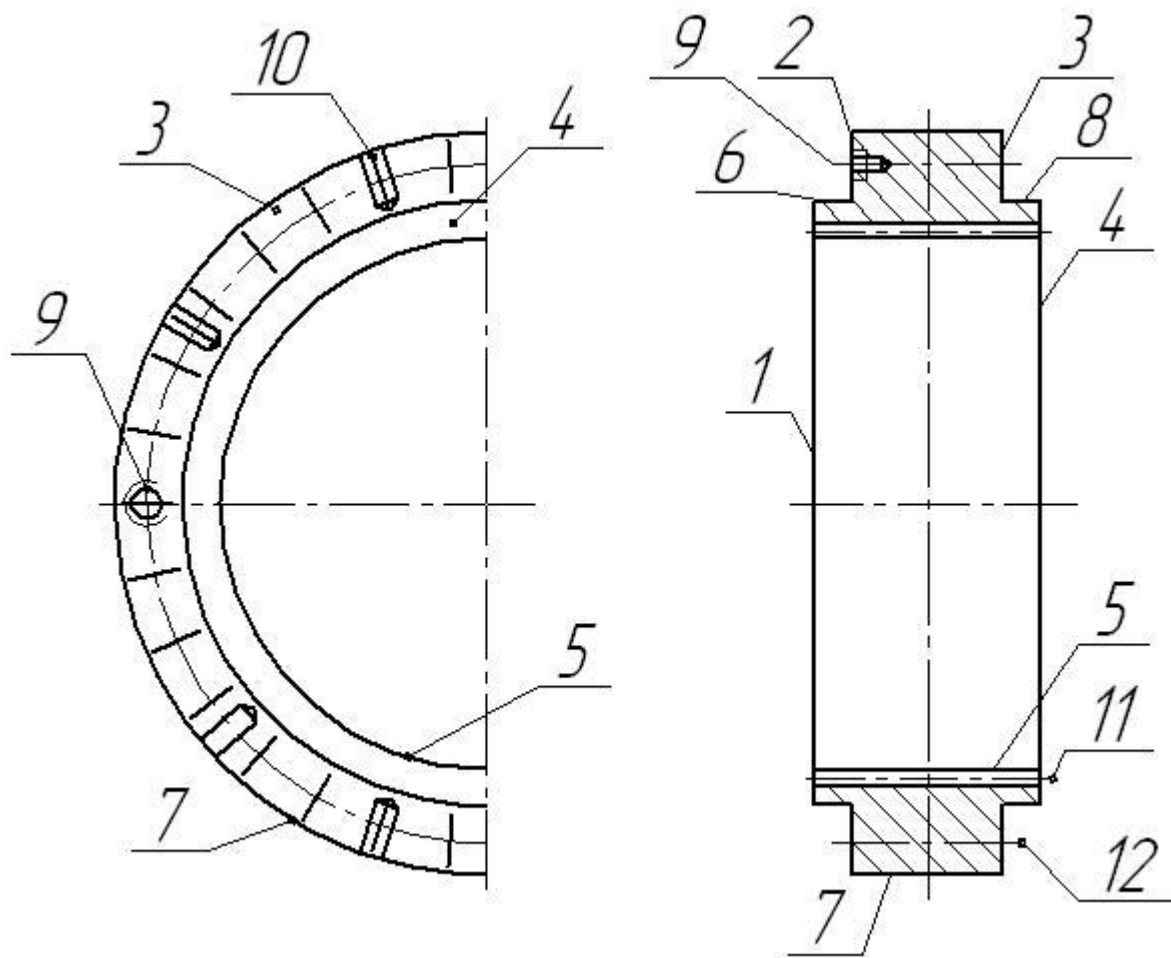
Эскиз шестерни - зубчатого колеса с внутренним зацеплением.
